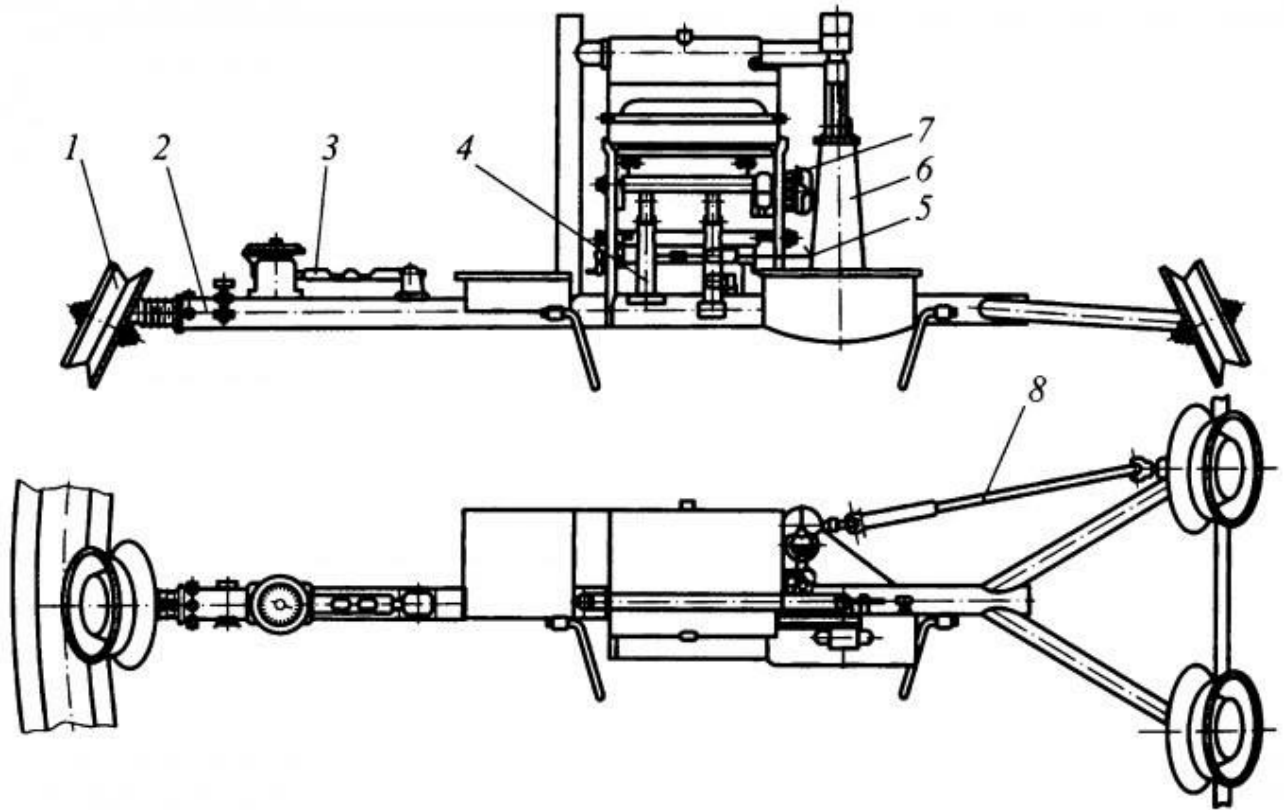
Триколісний колієвимірювальний візок конструкції Д. Д. Матвієнко: 1 – опорно-вимірювальне колесо; 2 – трубчаста рама; 3 – рідинний рівень; 4 – тримач механізму шаблону; 5 – тяга маятника; 6 – маятник; 7 – стрічкопротяжний механізм; 8 – карданна передача.
